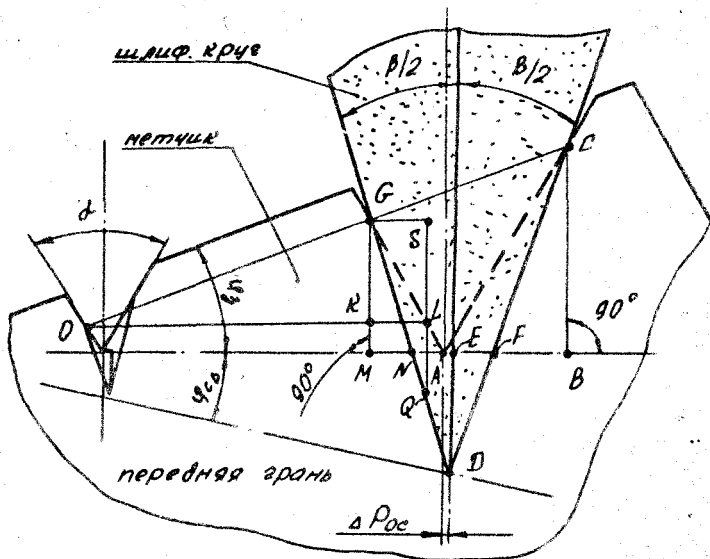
Способ изготовления с осевым смещением шлифовального круга
